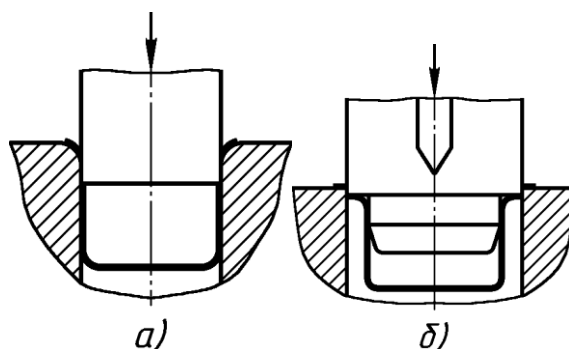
Обрезка в штампе заготовок без фланца (а) и с фланцем (б)
